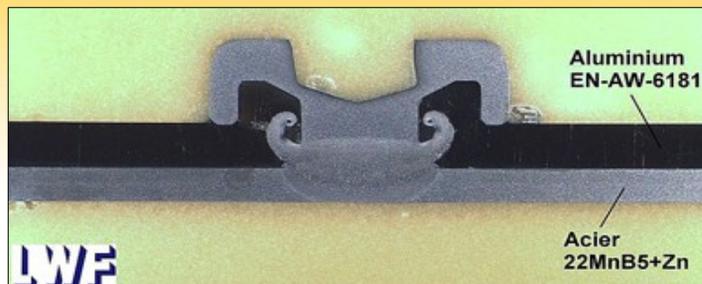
soudage par friction avec élément (source: Laboratory of Materials and Joining Technology, l'université de Paderborn)
